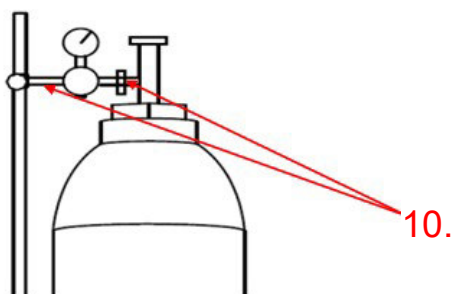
Einrichtung und Installation MIG Schweißgerät
